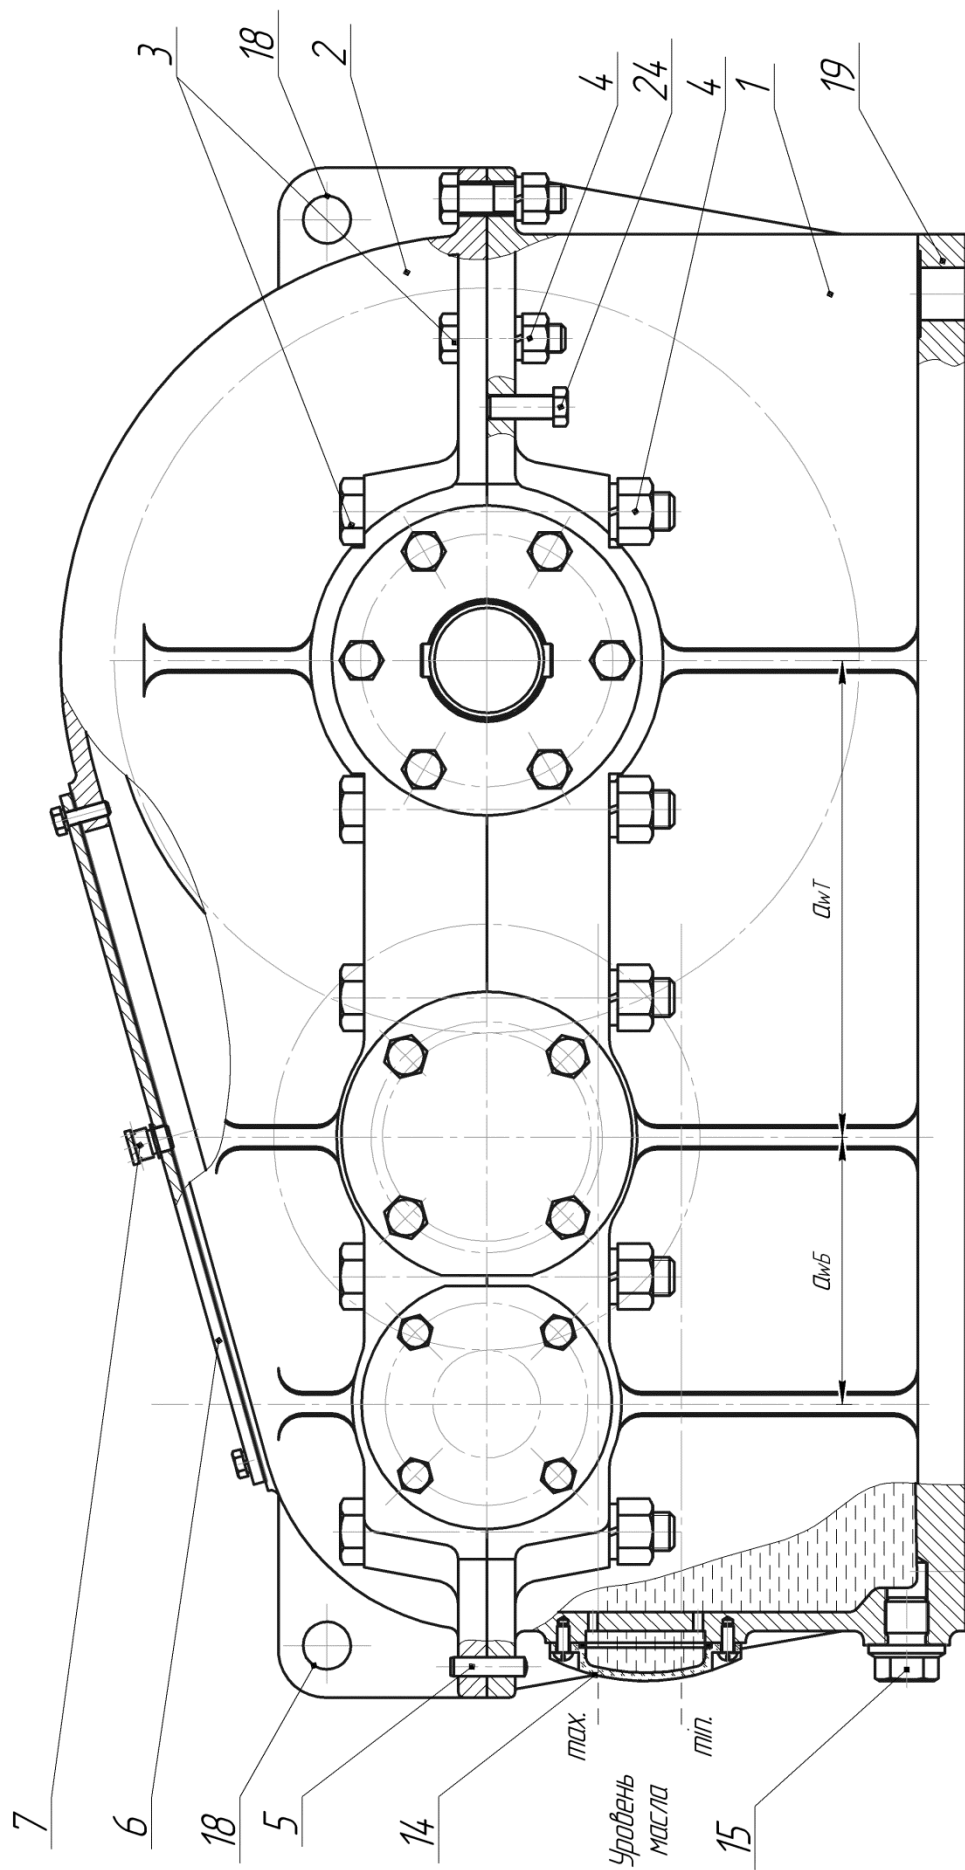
Конструкция двухступенчатого цилиндрического редуктора (главный вид)
